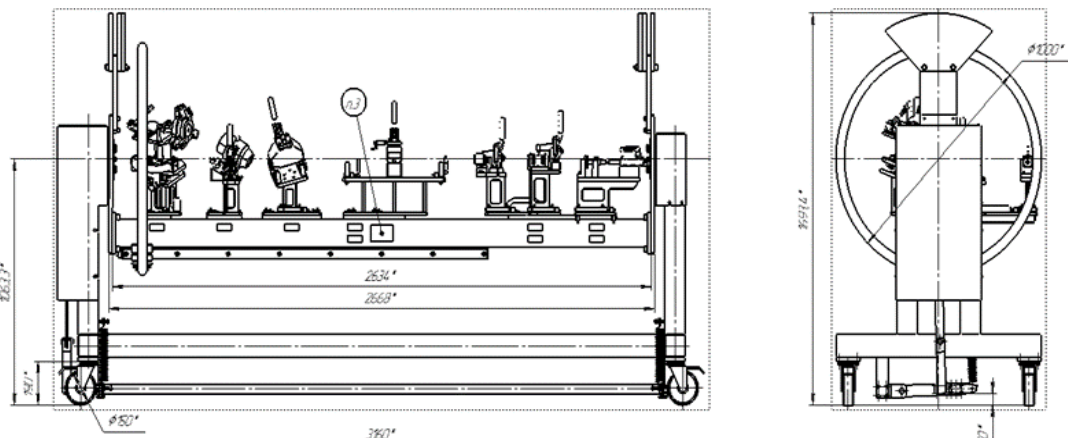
Схема устройства кондуктора для сварки сборки глушителей
